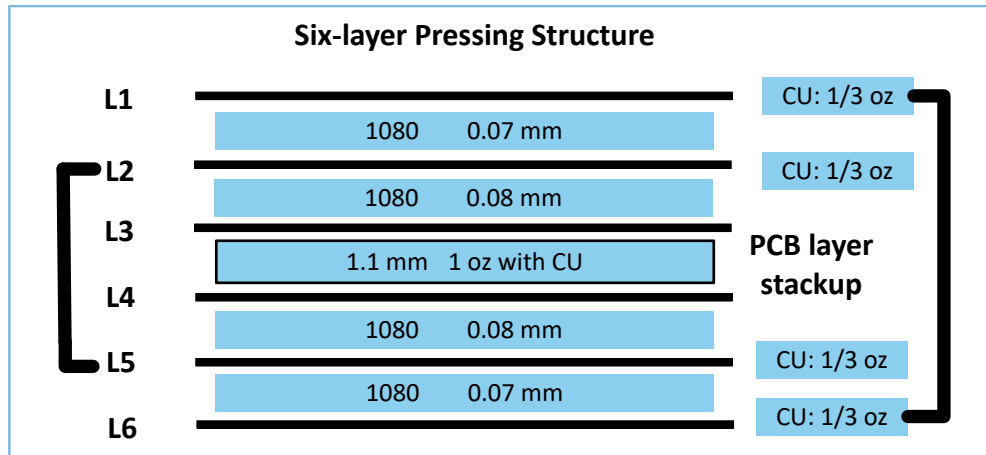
GR5526 PCB推荐叠层结构（BGA83）
